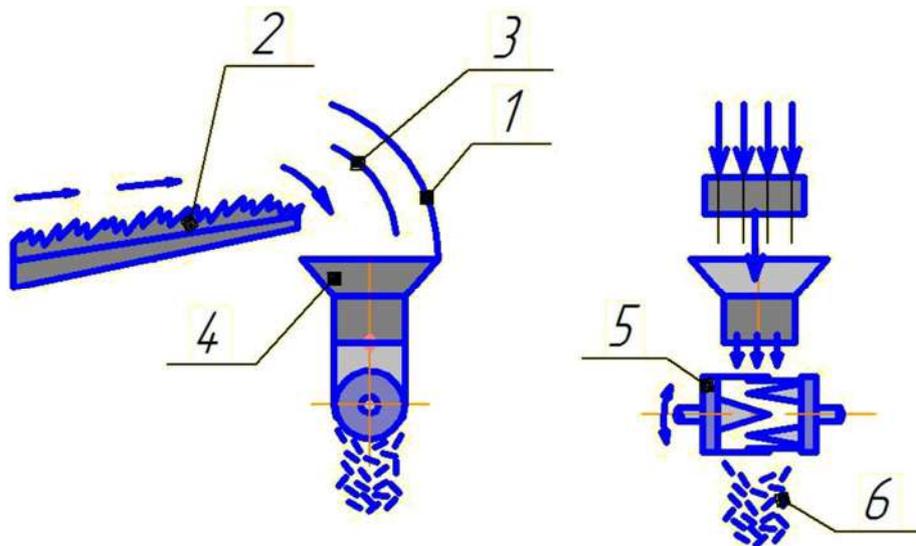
Технологический процесс работы и конструкция предлагаемого измельчителя-разбрасывателя соломы для зерноуборочного комбайна:
